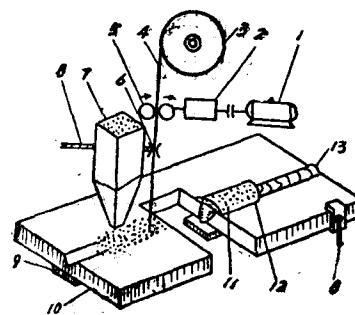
5 埋弧自动焊的焊接过程示意图
